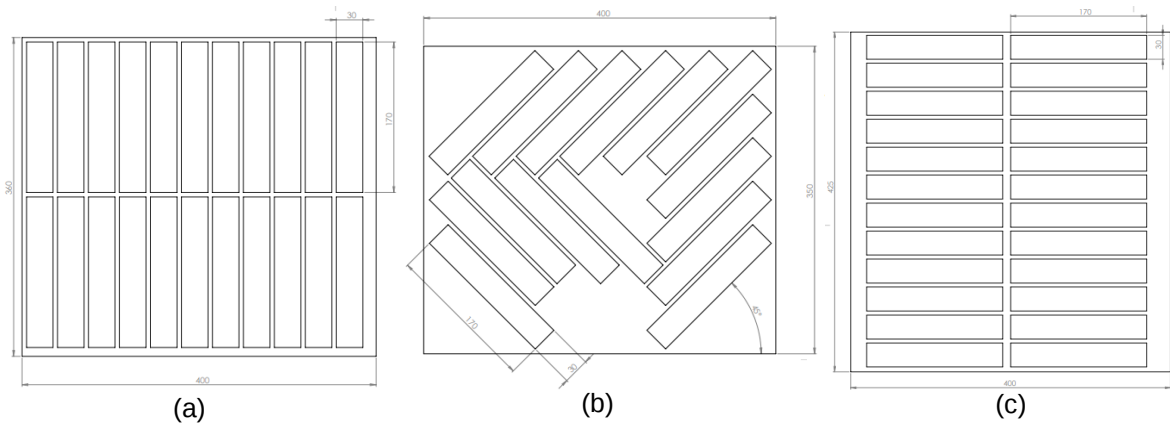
Desenho esquemático do plano de corte a laser das amostras de DC06
